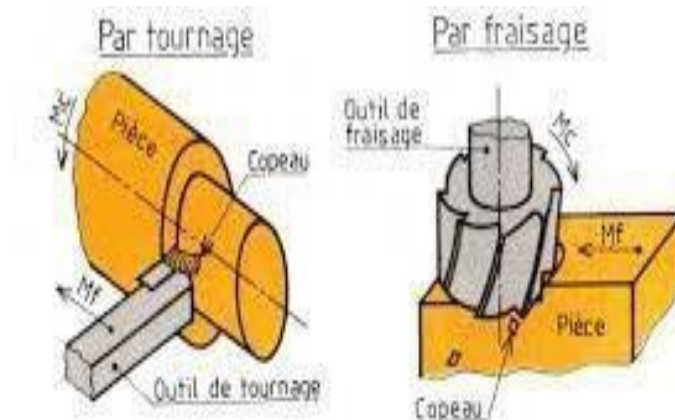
Mouvements de coupe et d'avance en tournage et fraisage 11
